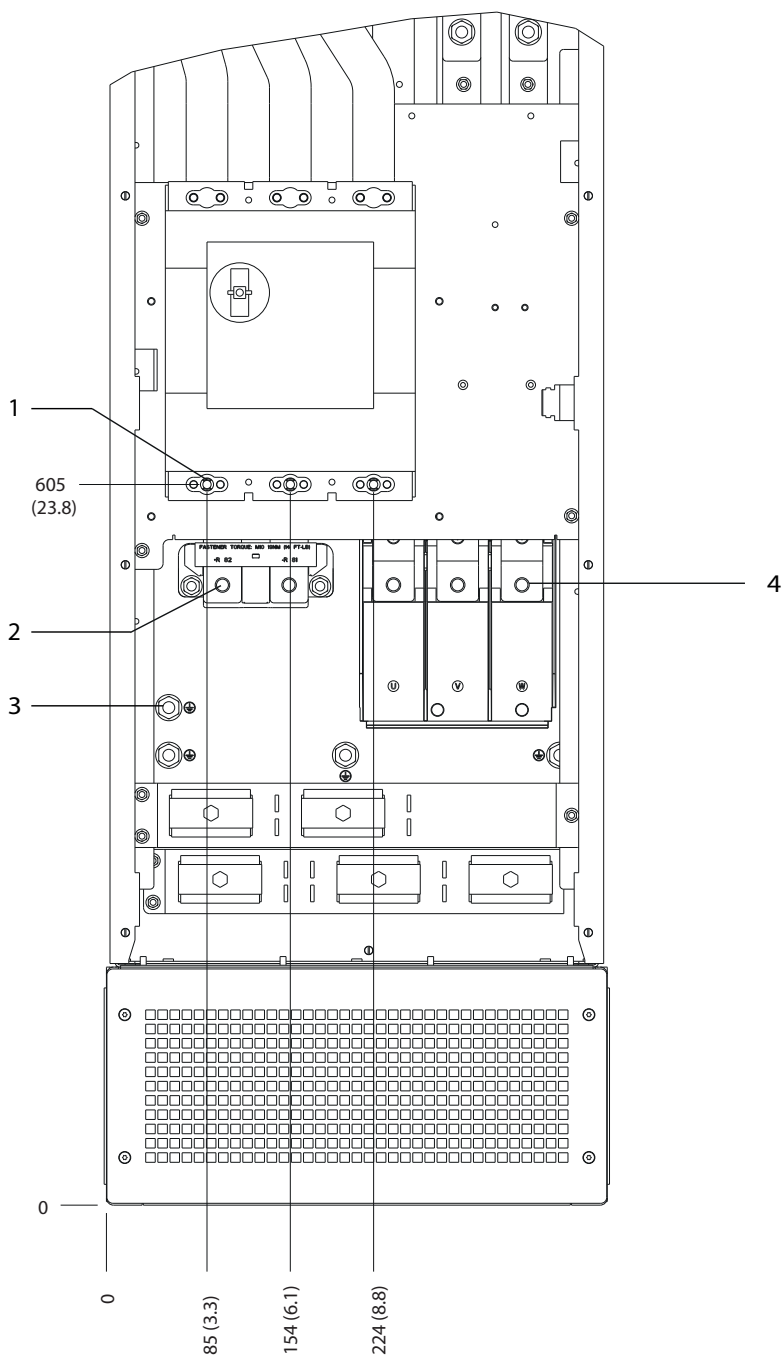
Dimensiunile bornelor pentru D8h cu opțiuni pentru contactor și separator (vedere frontală)
